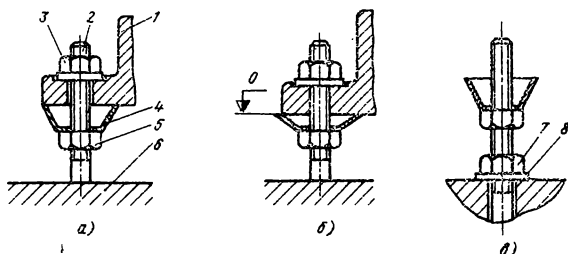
Установка оборудования с выверкой на установочных гайках:
